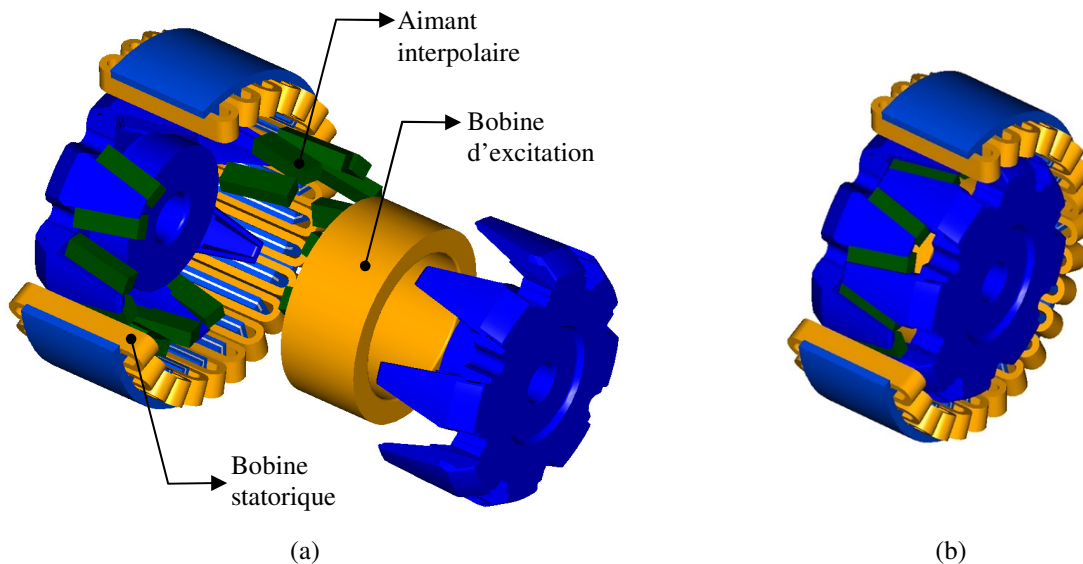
Vue éclatée de la machine à griffes 7-phases étudiée (a), et vue assemblée pour $\frac{3}{4}$ du stator (b)
